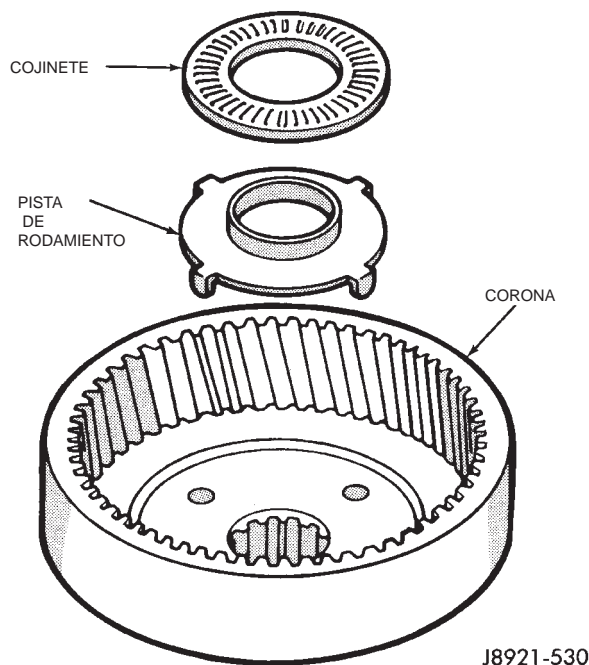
Instalación del cojinete y la pista de rodamiento de la corona
